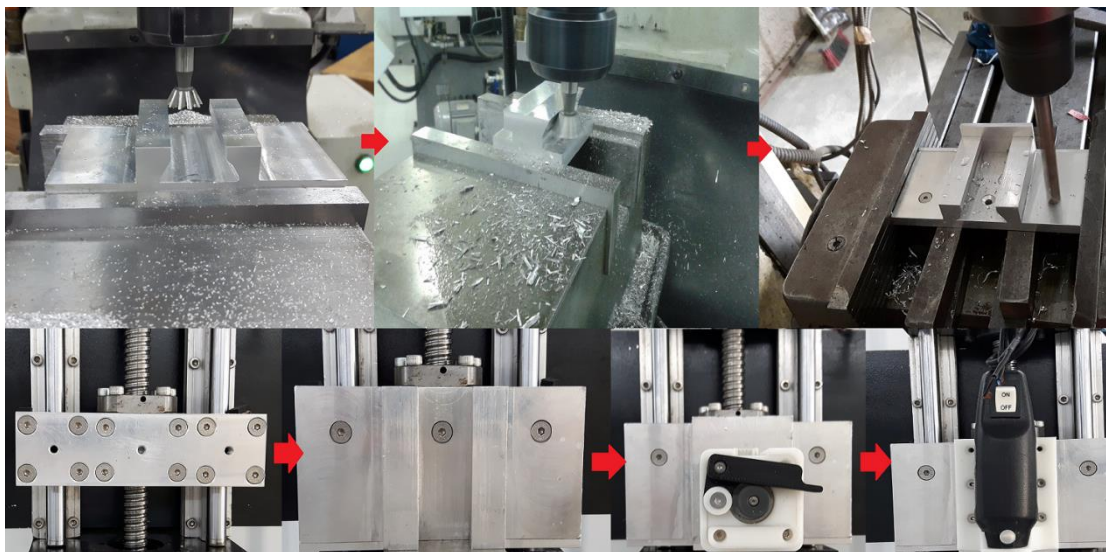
Processo de usinagem e instalação do suporte de ferramenta.
